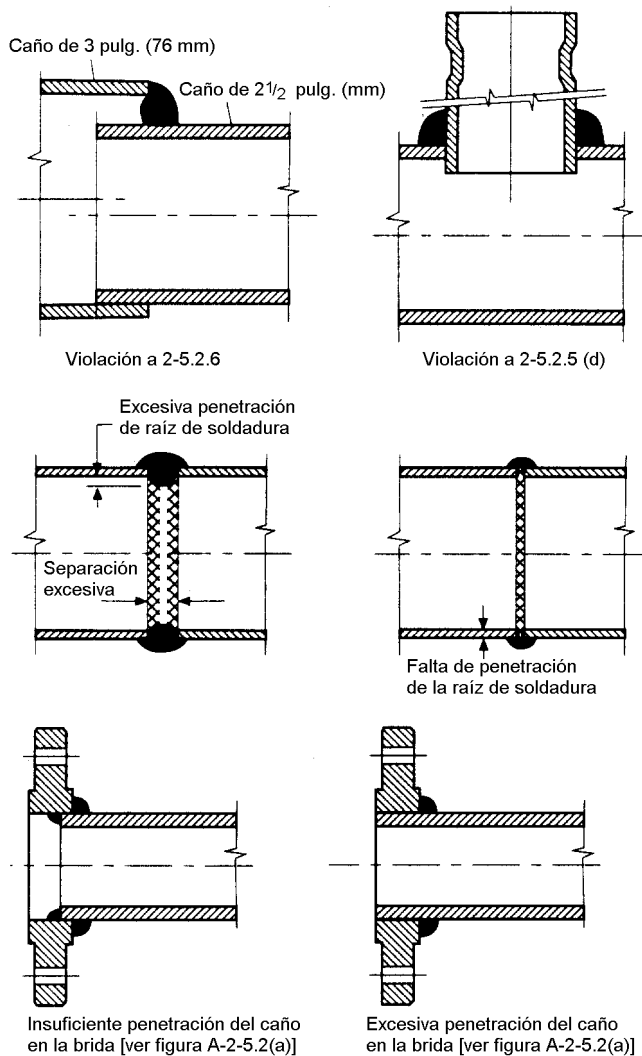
(b) Uniones soldadas inaceptables.
